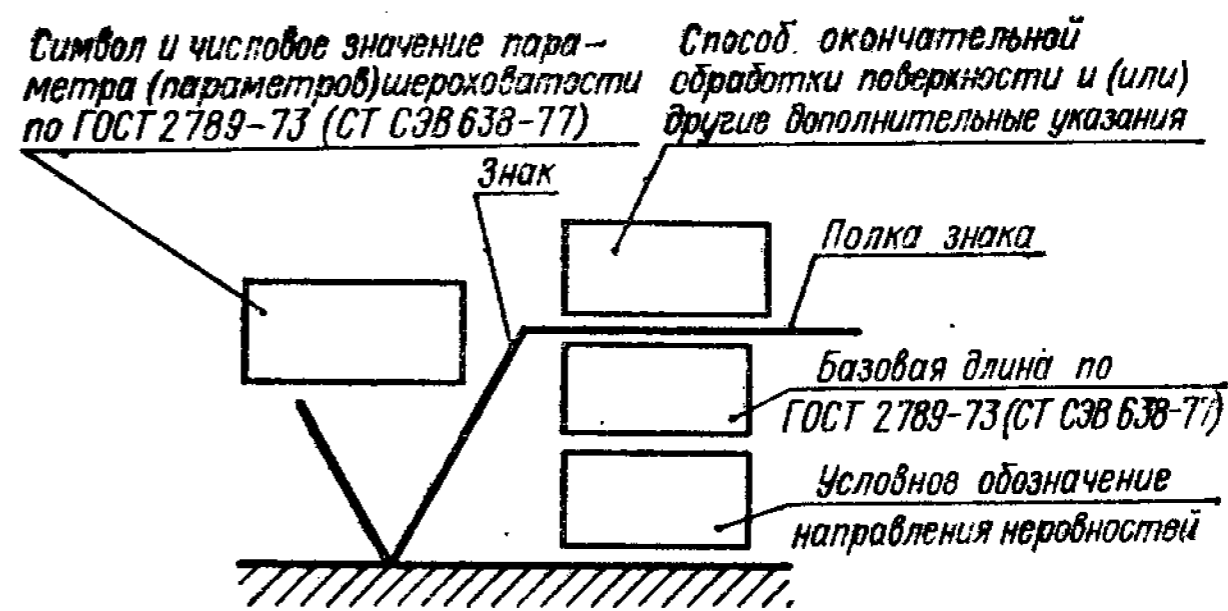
Структура обозначения шероховатости поверхностей на чертежах
